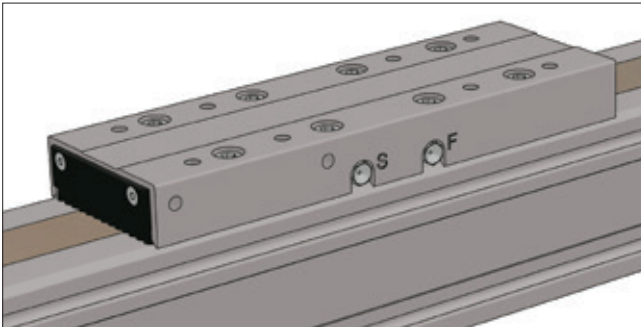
Schlitteneinheit mit Gewindebohrungen
